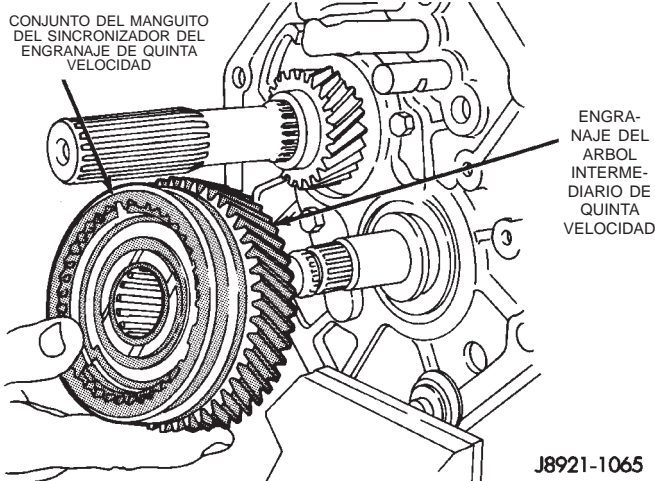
Desmontaje del conjunto del engranaje de quinta velocidad y el sincronizador
